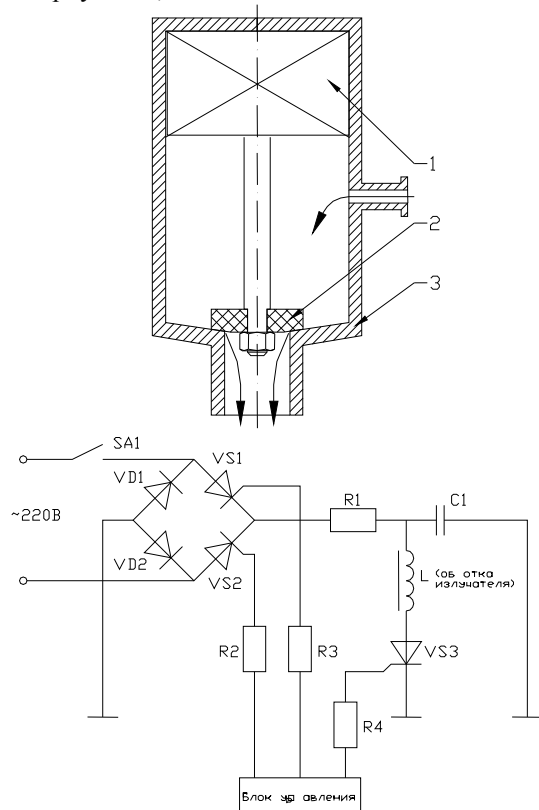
Схематический вид излучателя с электро-схемой питания. 1 – электромагнит, 2 – запорный элемент излучателя, 3 – герметичный корпус
